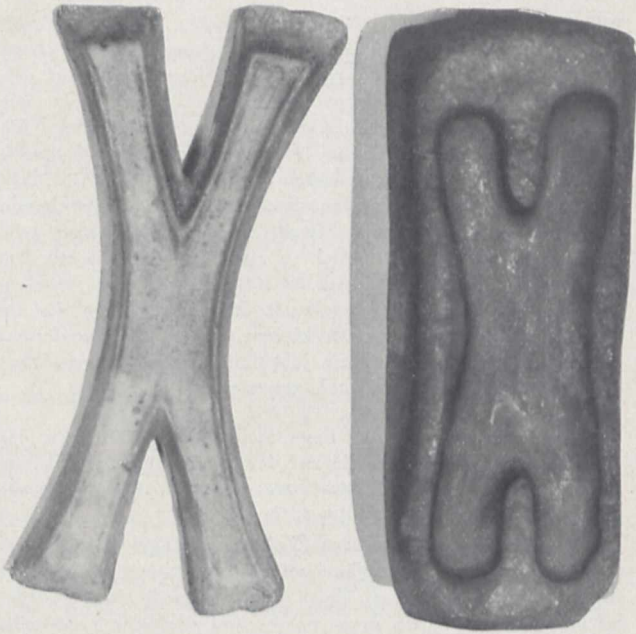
Geldstück in Form eines Kupferkreuzes; daneben eine Form zum Gießen des Geldes, gefunden in Simbabwe
